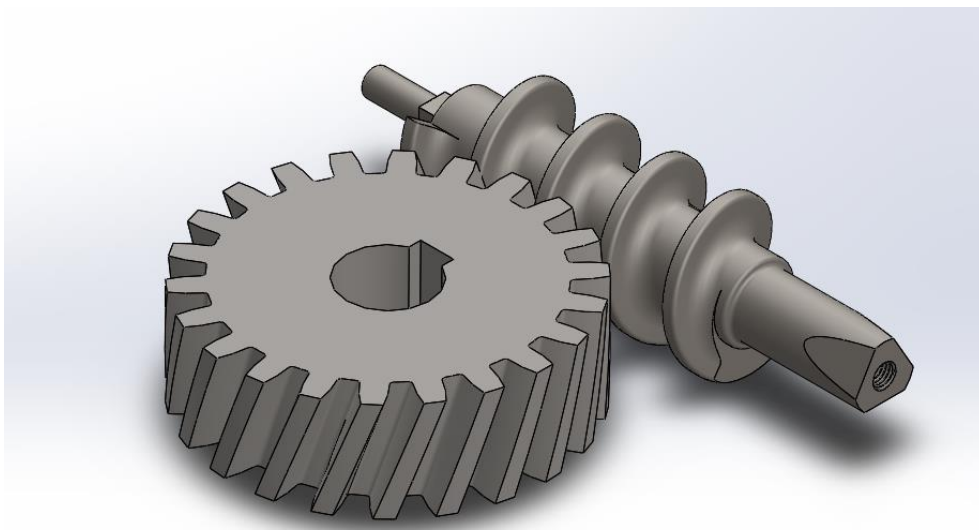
Engranaje de 22 dientes y sinfín.
